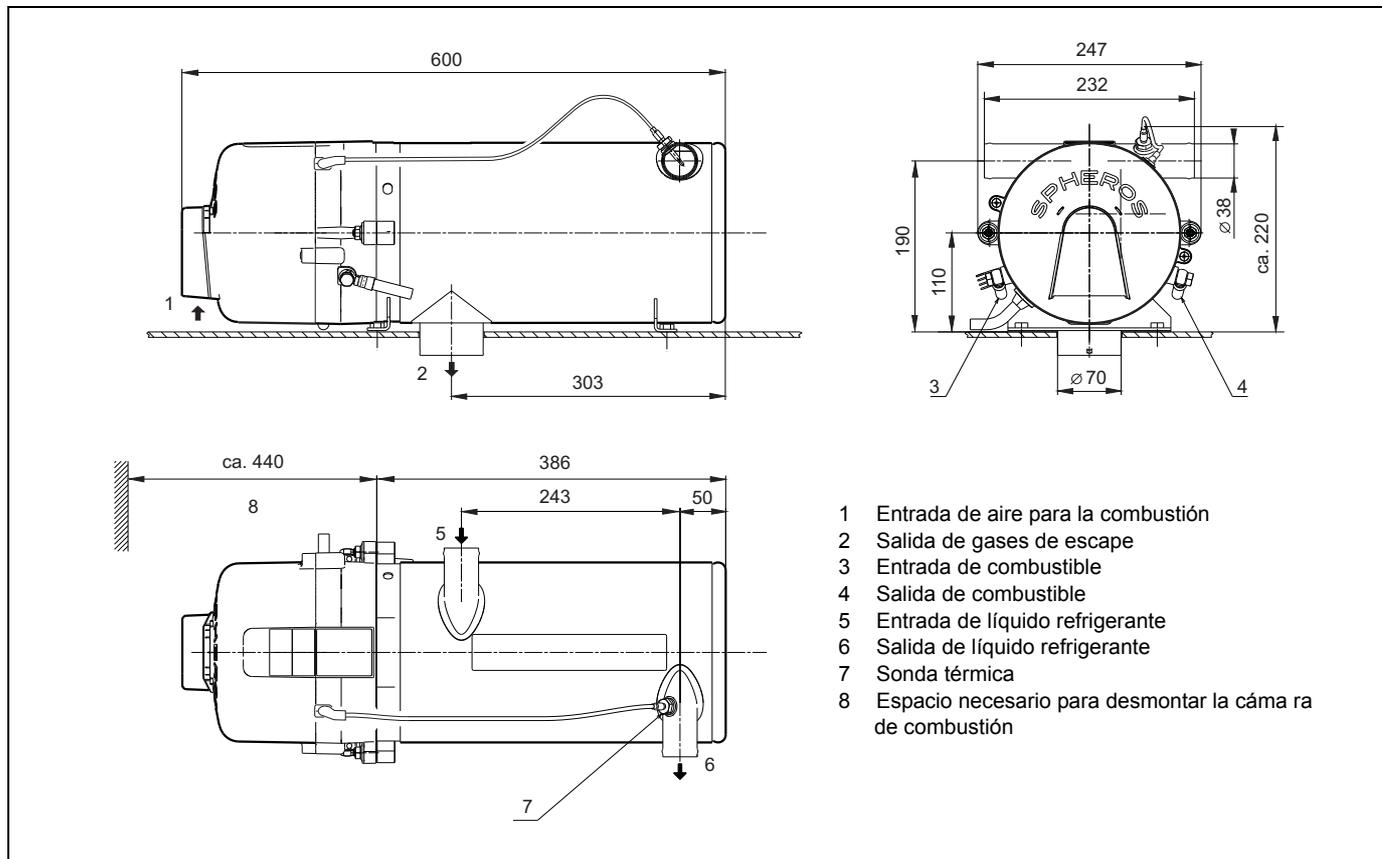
Dimensiones del calefactor Thermo S 160/230/300/350/400 (montaje horizontal)
